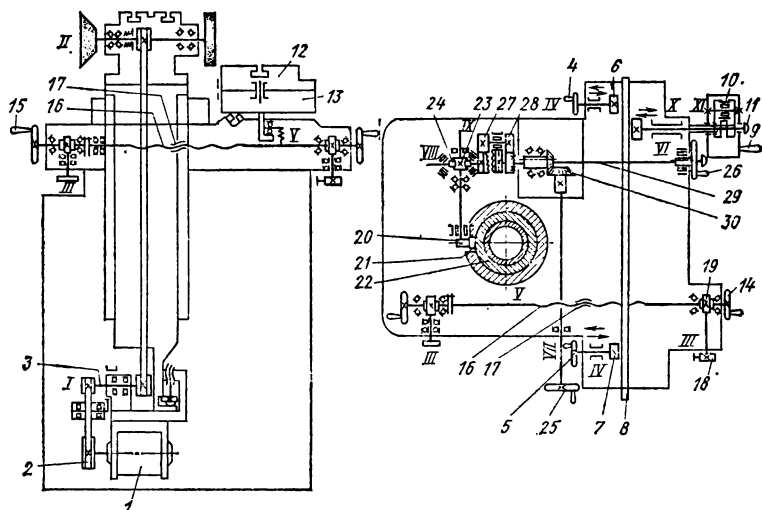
Кинематическая схема универсально-заточного станка мод. 3B642: 1 — электродвигатель; 2 — шкив; 3 — редуктор; 4, 5, 9, 14, 15, 18, 25 и 26 — маховички; 6 и 7 — шестерни; 8 — рейка; 10 — планетарный механизм; 11 — кнопка; 12 — поворотный стол; 16 — ходовой винт; 17 — гайка; 19, 29 и 30 — шестерни; 20 и 21 — реечная пара; 23 — червячный редуктор; 24 — червяк; 27 — планетарный механизм; 28 — муфта
